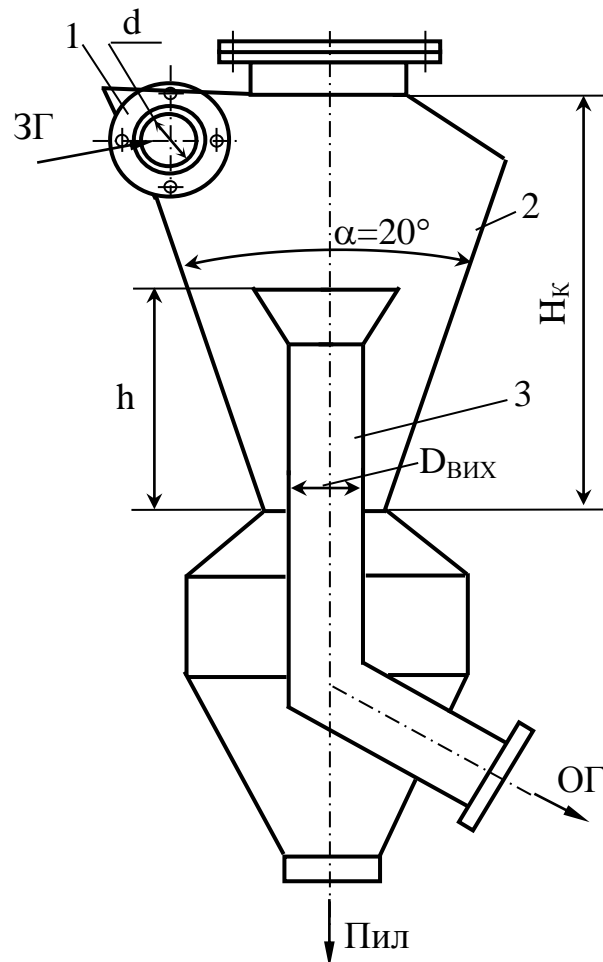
Конструктивна схема прямооточного циклона типу НВГК: 1 – тангенціальний патрубок; 2 – конусний корпус; 3 – вихлопна труба очищеного газу
